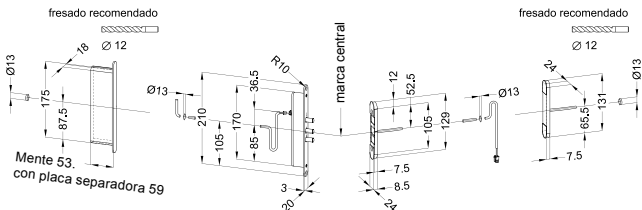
medidas para contacto pasacorriente de pieza de la hoja con pletina F20 y pieza del marco con tapa terminal
